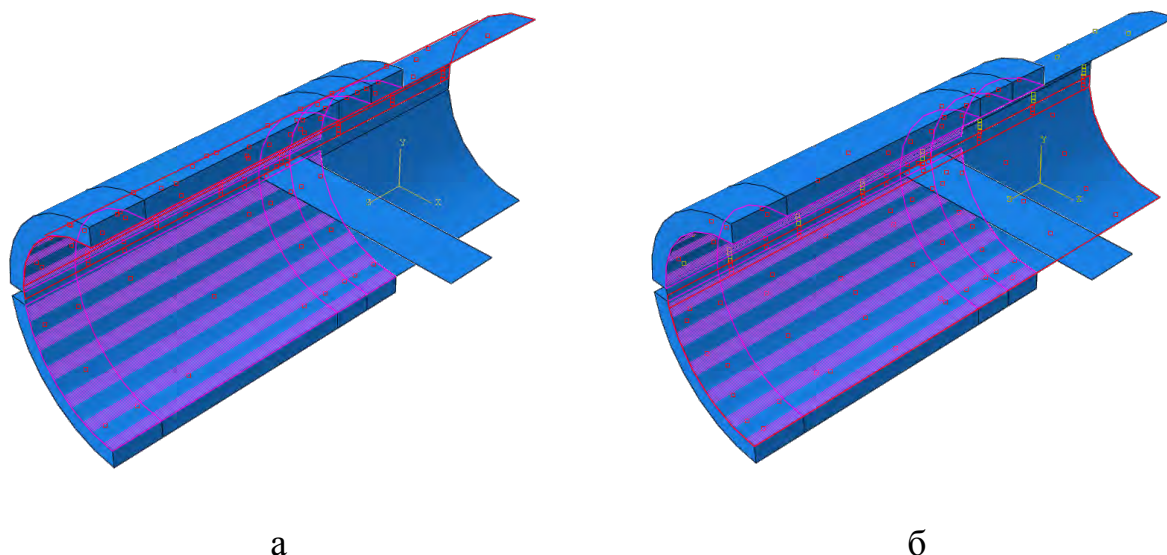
Контактное взаимодействие поверхностей верхнего (а) и нижнего (б) приспособления с внутренней поверхностью образца
